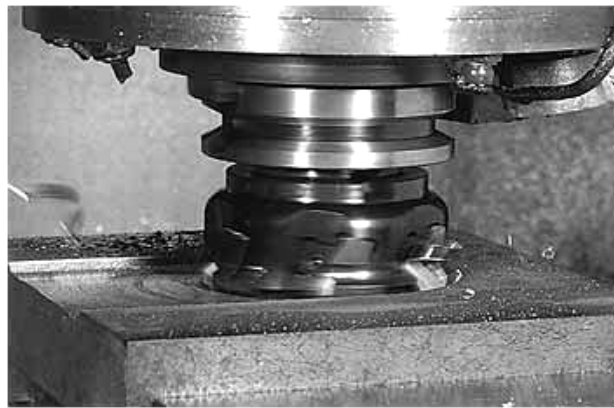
Процес обробки деталей торцевими фрезами *Double Mill
